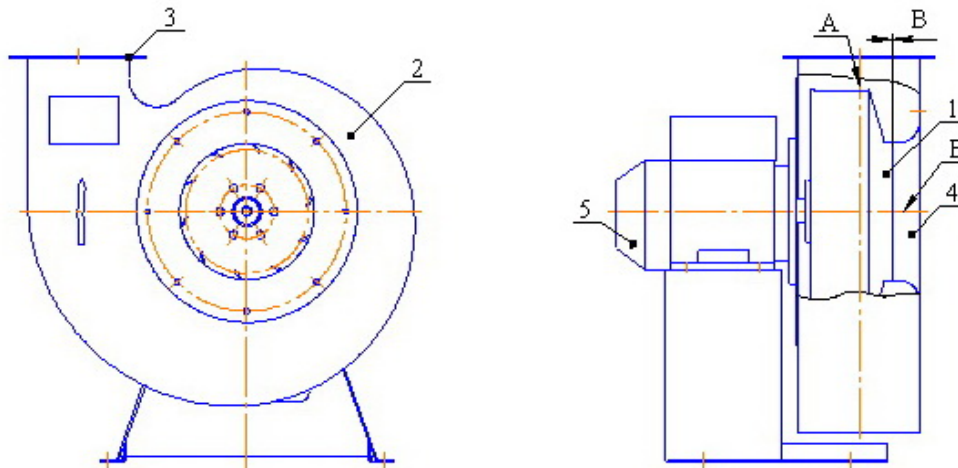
Вентиляторы ВРП-100-45-3,15. Конструкция и состав.
